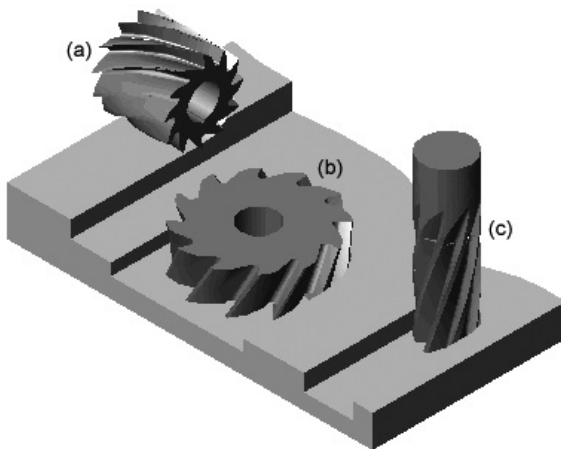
| Tipos de fresa: (a) cilíndrica horizontal; (b) fresa de disco; (c) fresa cilíndrica vertical (ou de topo)
